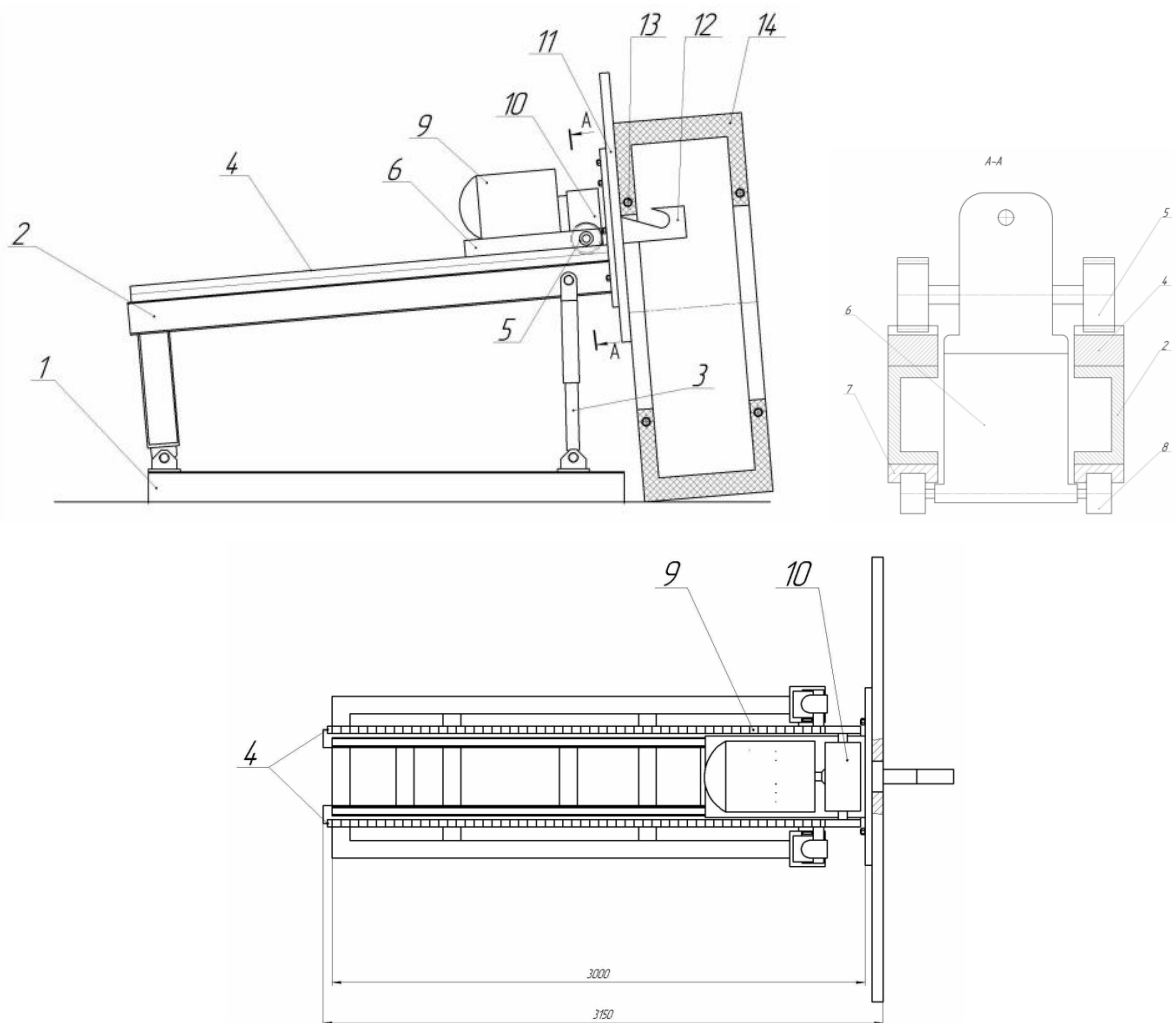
Общий вид установки для извлечения бортовых колец [98]
